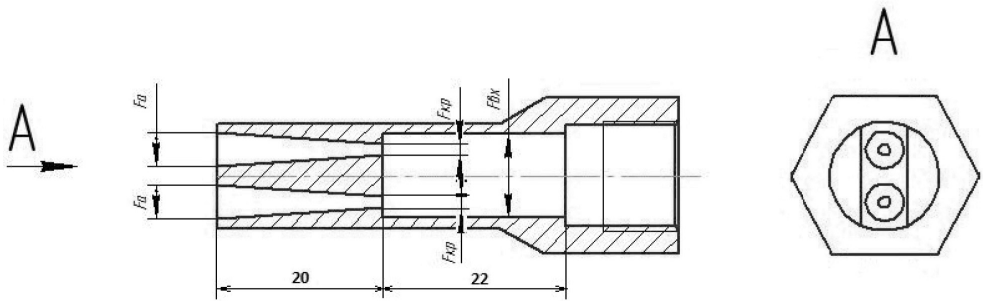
Сверхзвуковое сопло металлатора ЭДМ-11ШД
